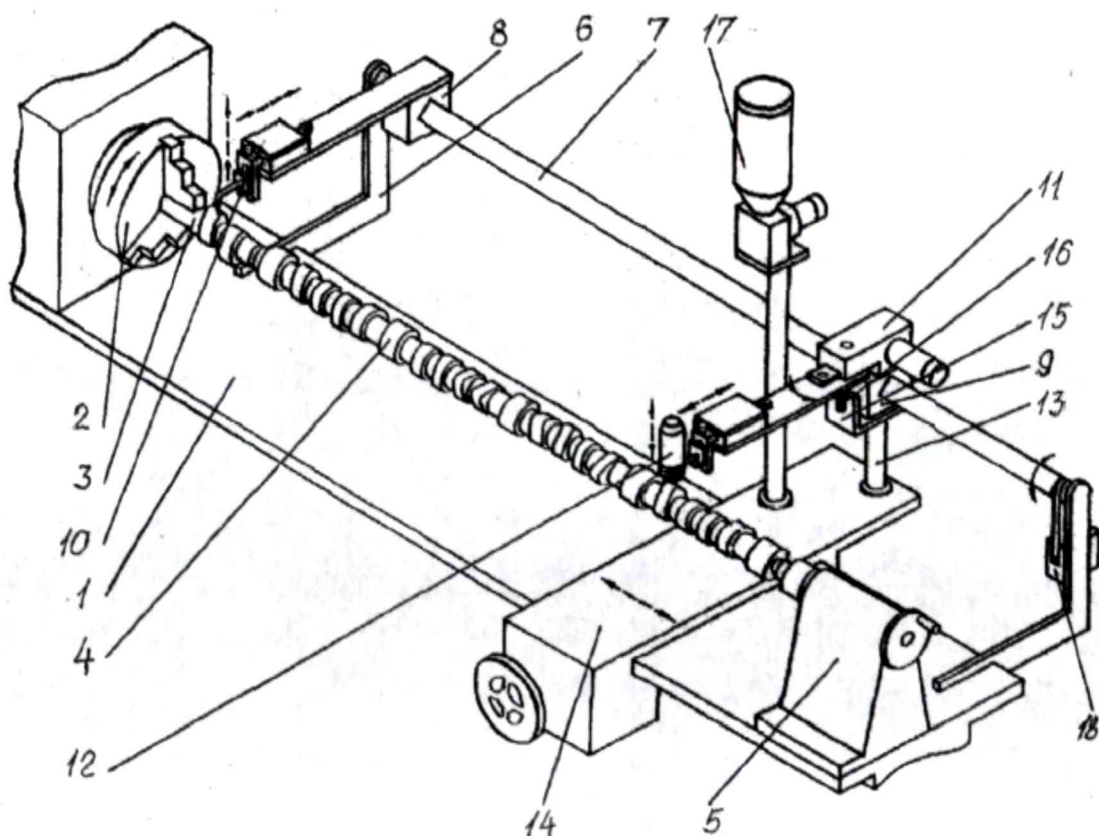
Загальний вид копіювального обладнання 1 - станина; 2 - патрон; 3 - копір; 4 - розподільний вал; 5 – задня бабка; 6 - кронштейн; 7 - напрямна; 8 - опорна каретка; 9 – робоча каретка; 10 - опорний елемент; 11 - механізм коливань; 12 - плазмотрон; 13 - стійка; 14 - позовжній супорт; 15 - вилка; 16 - палець; 17 – порошковий живильник; 18 - командоапарат.
